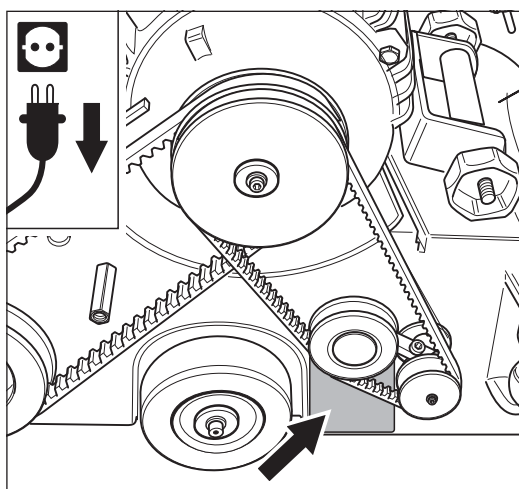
Maschinen-Typenschild am Maschinengehäuse unterhalb des Keilriemenspanners.
